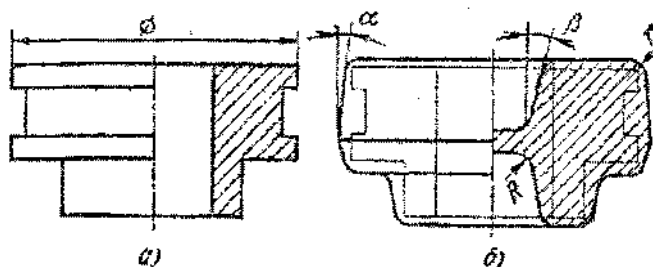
Пример составления чертежа поковки: а - деталь; б – поковка
